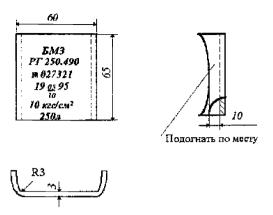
Образец таблички с указанием паспортных данных резервуара
